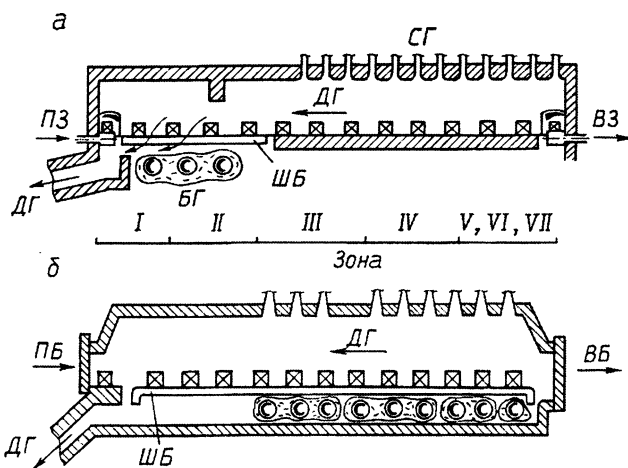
Схема нагревательной печи с шагающими балками и шагающим подом стана 320 (а) и нагревательной печи с шагающими балками стана 850 (б) Белорусского металлургического завода: ПЗ, ПБ – посад заготовок и блювы; ВЗ, ВБ – выдача; СГ, БГ – сводовые и боковые горелки; ШБ – шагающие балки; ДГ – дымовые газы
